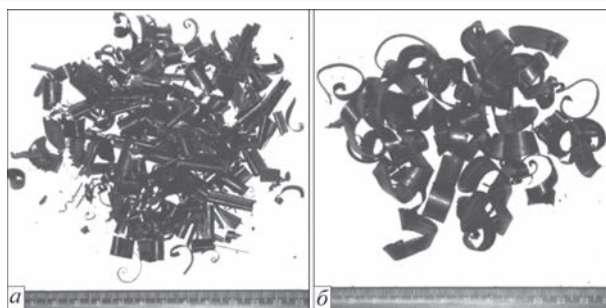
Стружка стали 5ХНМ с фрезерных (а) и строгальных (б) станков
